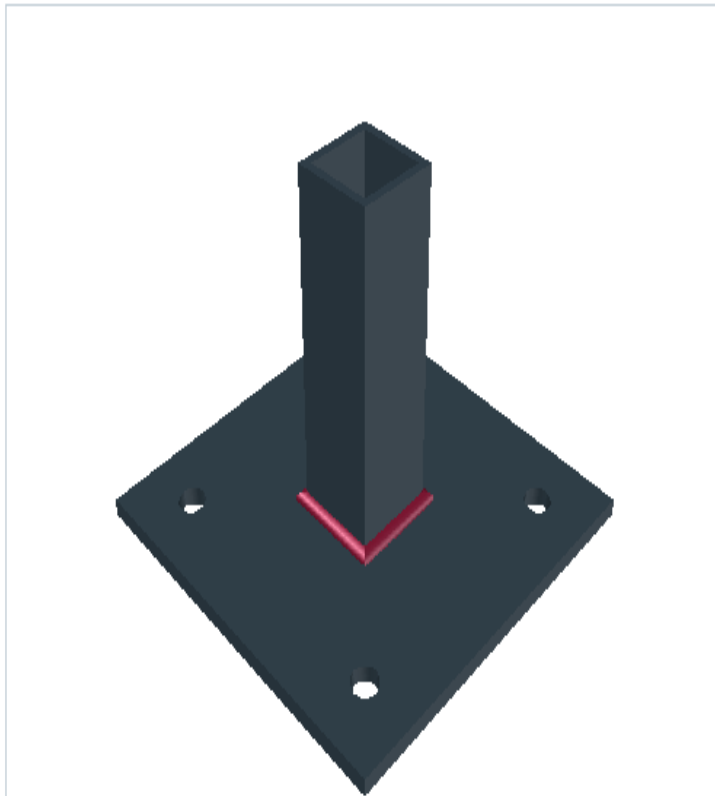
Junta de soldadura en te del elemento viga
